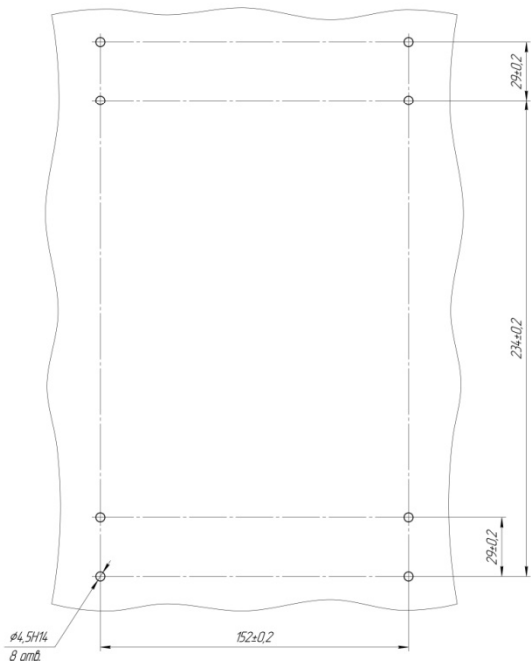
Габаритные и присоединительные размеры устройства РС830-ДТ2 при внешнем монтаже, обеспечивающем его поворот влево/вправо
